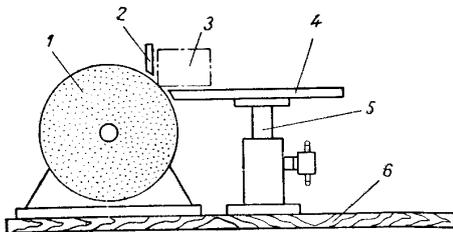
Шлифовальное зачистное приспособление:
